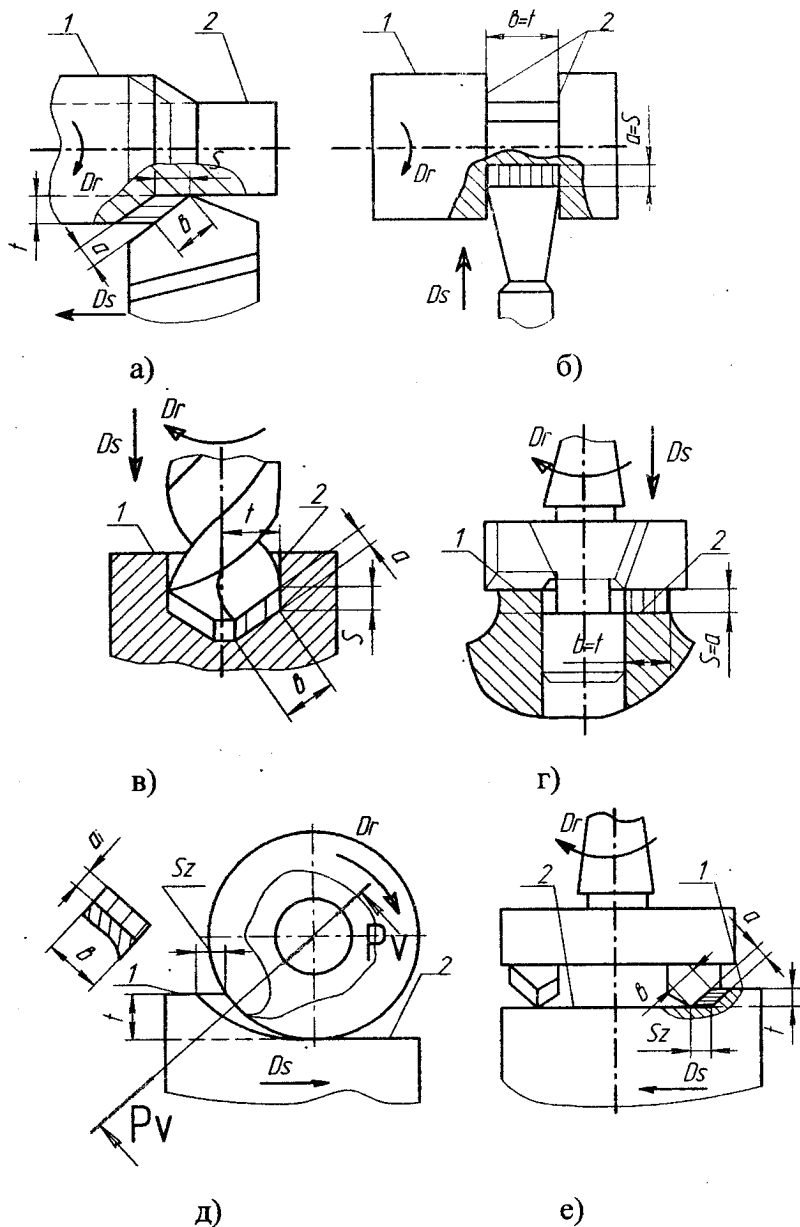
Типові схеми визначення глибини різання  $t$
